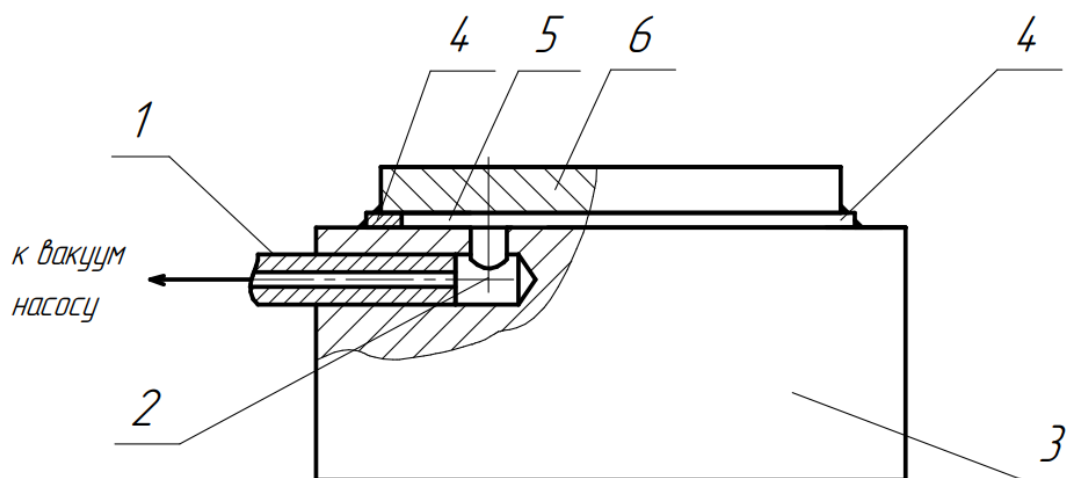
Схема вакуумирования сварных пакетов
